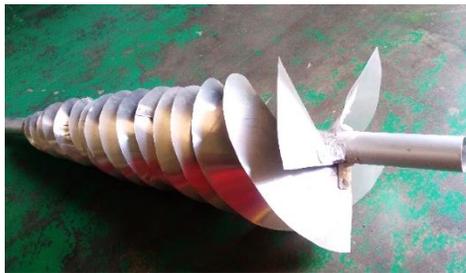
Hasil Manufaktur Turbin Spiral Sudu 3
